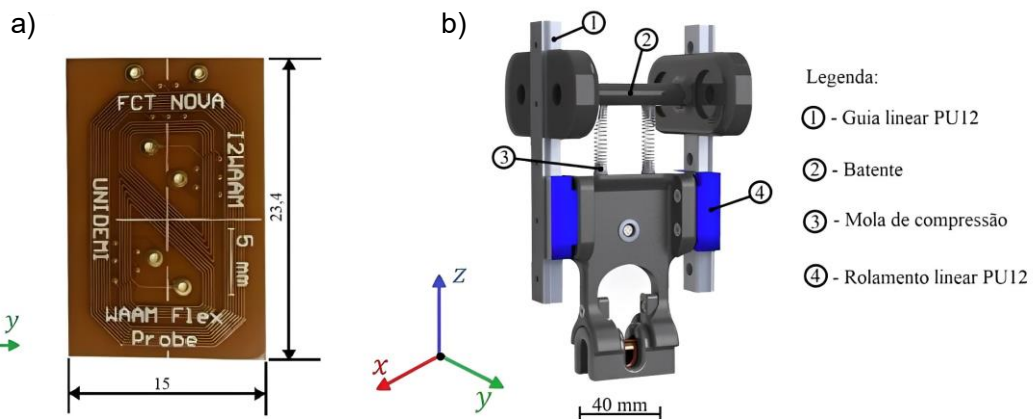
Sonda WFP em PCB flexível: (a) configuração do PCB flexível; (b) Chassis autocompensante [52]
